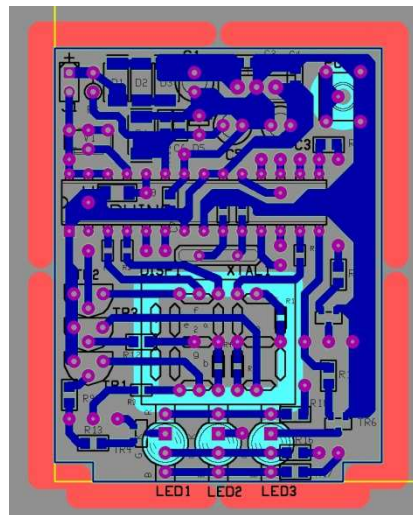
PCB con componenti SMD e layer per la realizzazione del pannello
